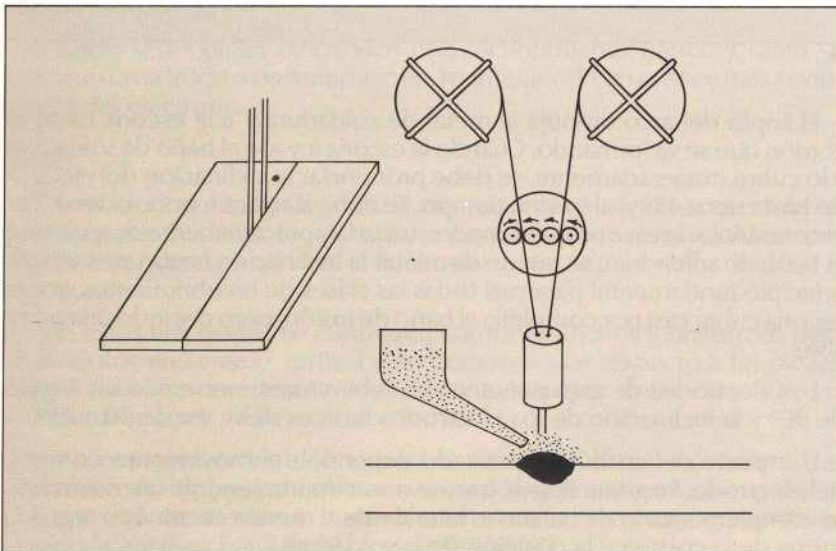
Soldadura por arco sumergido utilizando dos hilos.
